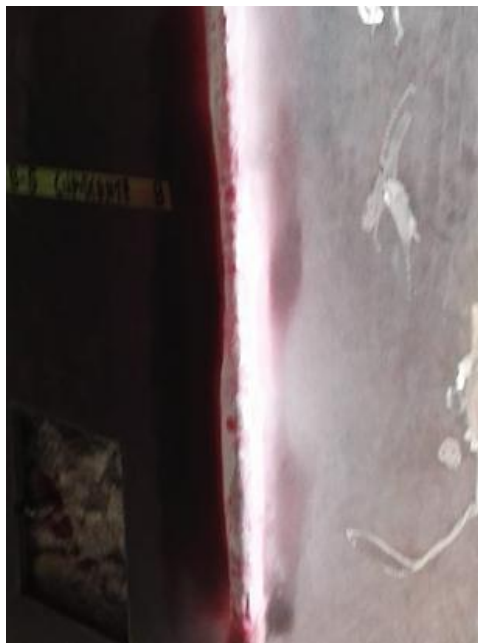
Reparación de los puntos de soldadura defectuosos.
